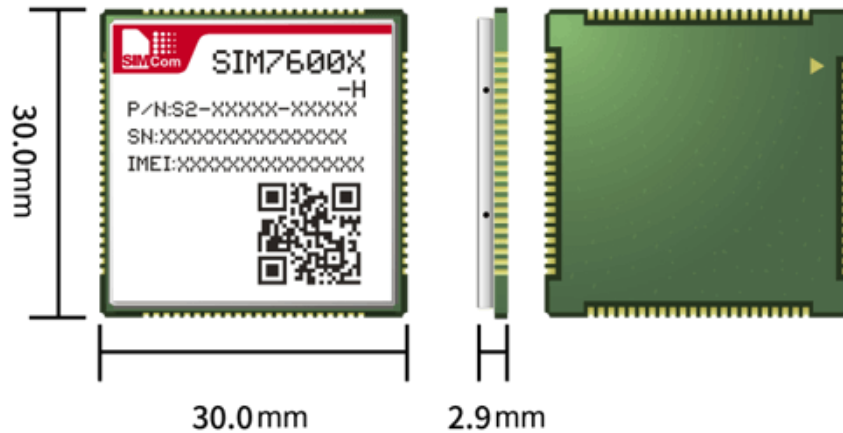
Dimensiones físicas del módulo SIM7600E-H.
